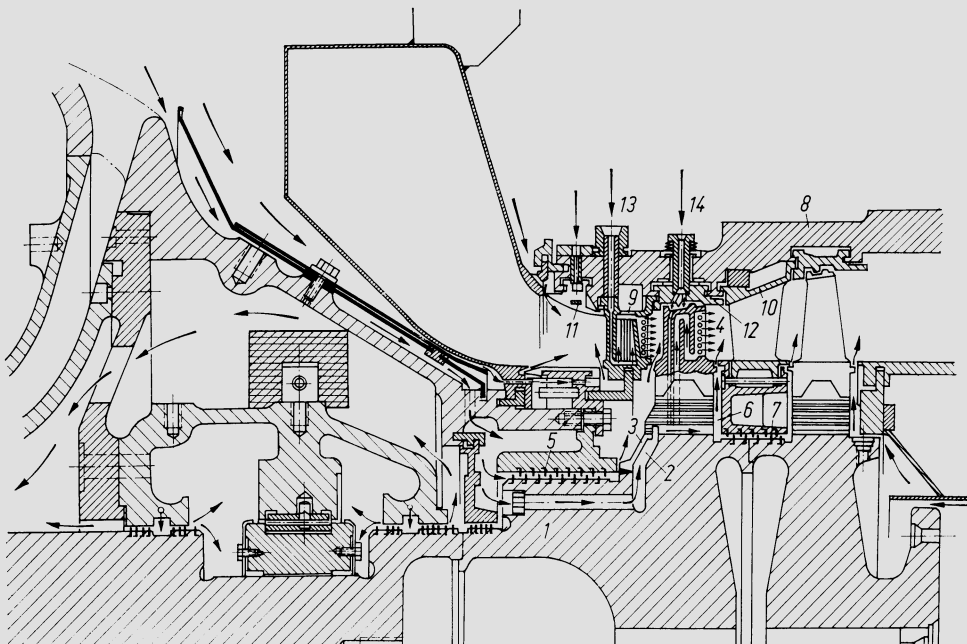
Kühlluftführung bei einer Gasturbine mit Scheibenrotor (Sulzer)
